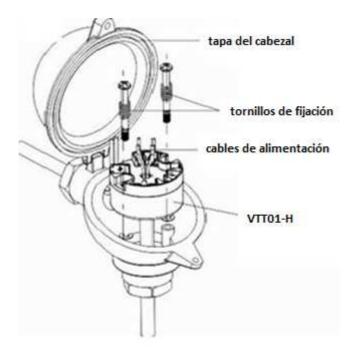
Esquema de montaje del VTT01-H en cabezal.
